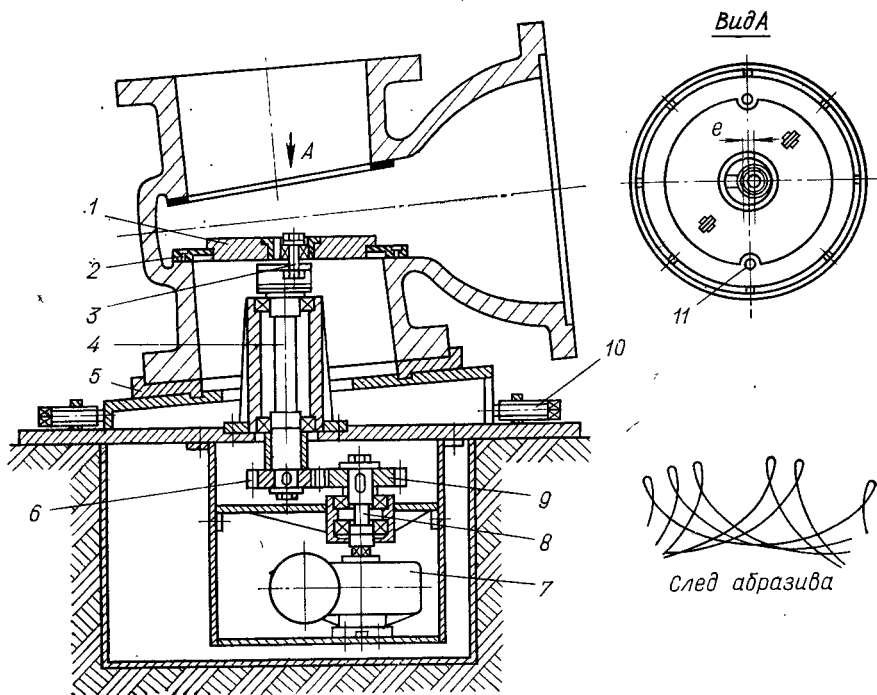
Станок для притирки уплотнительных колец корпуса задвижки:
